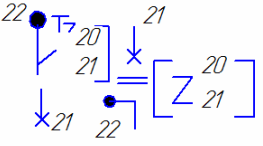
Схемы установки заготовок на цилиндрические и плоские поверхности:
